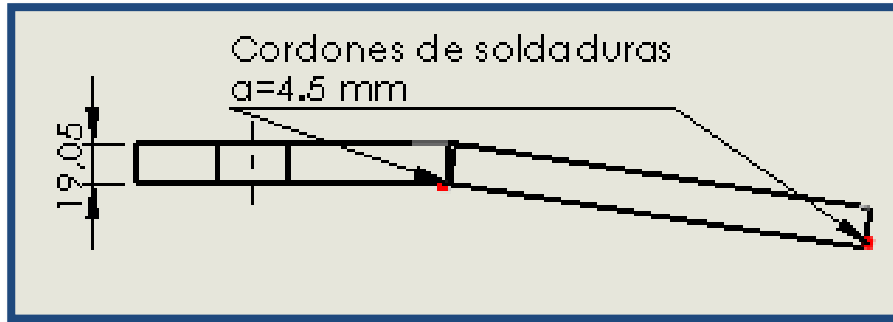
Vista de los cordones de soldadura realizados en el ojal trasero de la lanza.
